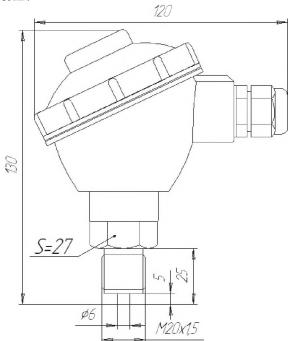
Модель 1015. Литой корпус. Гермоввод кабеля.
